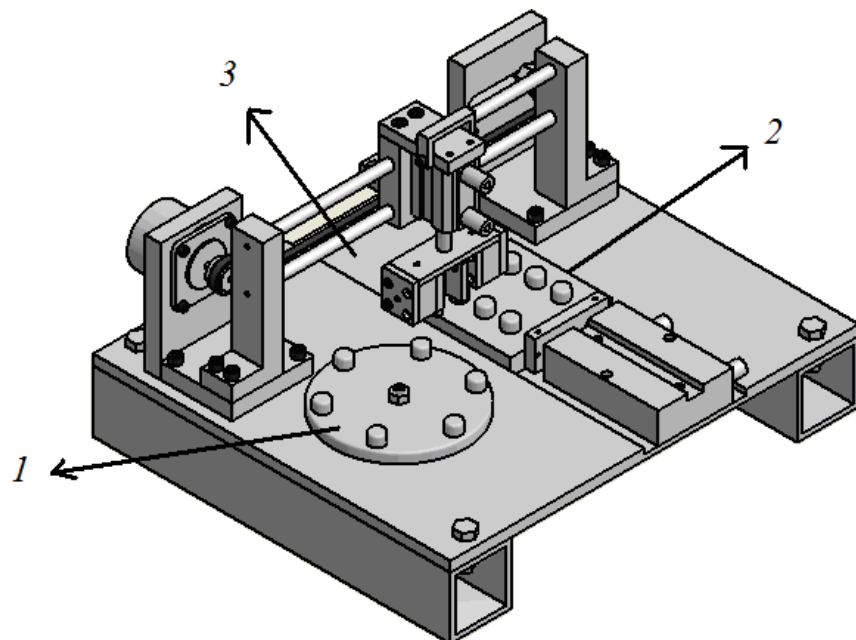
Розроблена CAD модель пакувальної машини
